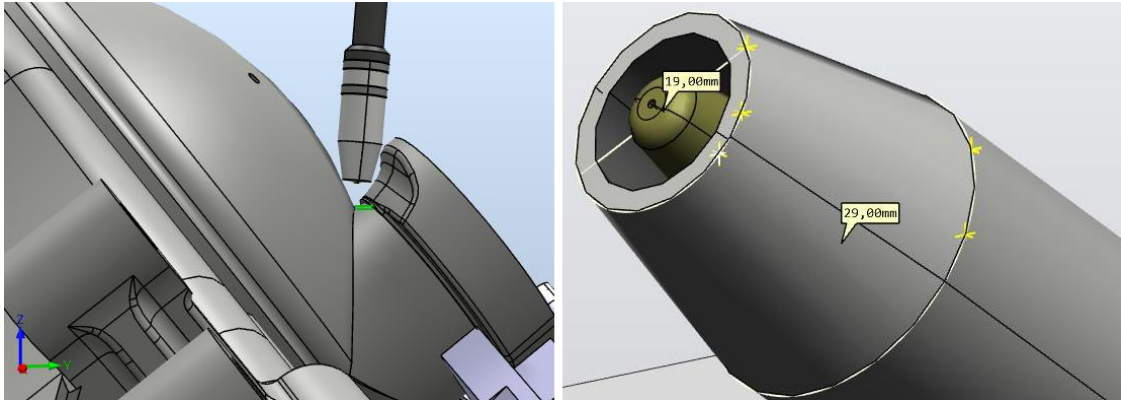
Restrição no diâmetro do bocal da tocha de soldadura
